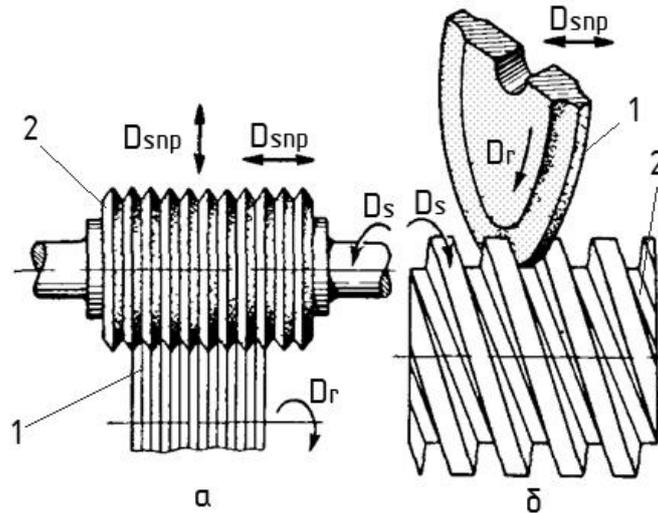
Схемы наружного шлифования резьбовых поверхностей
